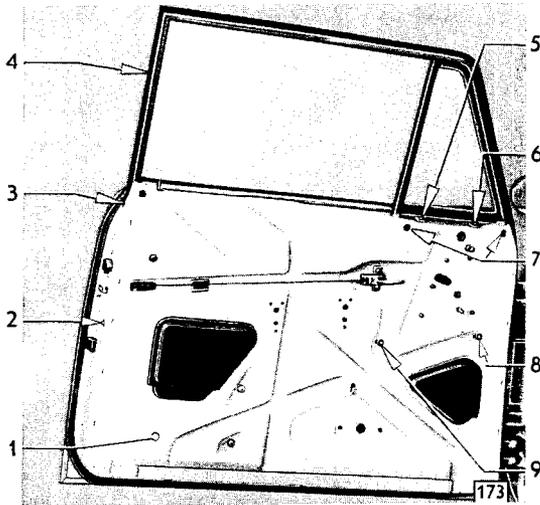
Lage der Schrauben, die bei Ausbau des Fensterrahmens herausgeschraubt werden müssen
